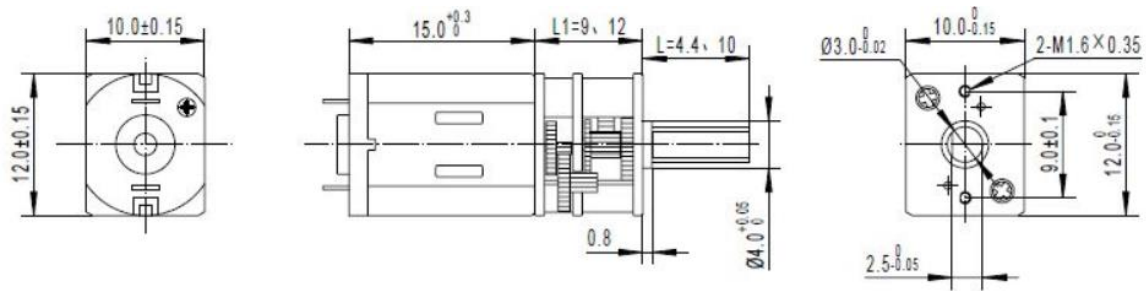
Dimensiones (mm) del motor N20 con caja reductora lineal.
